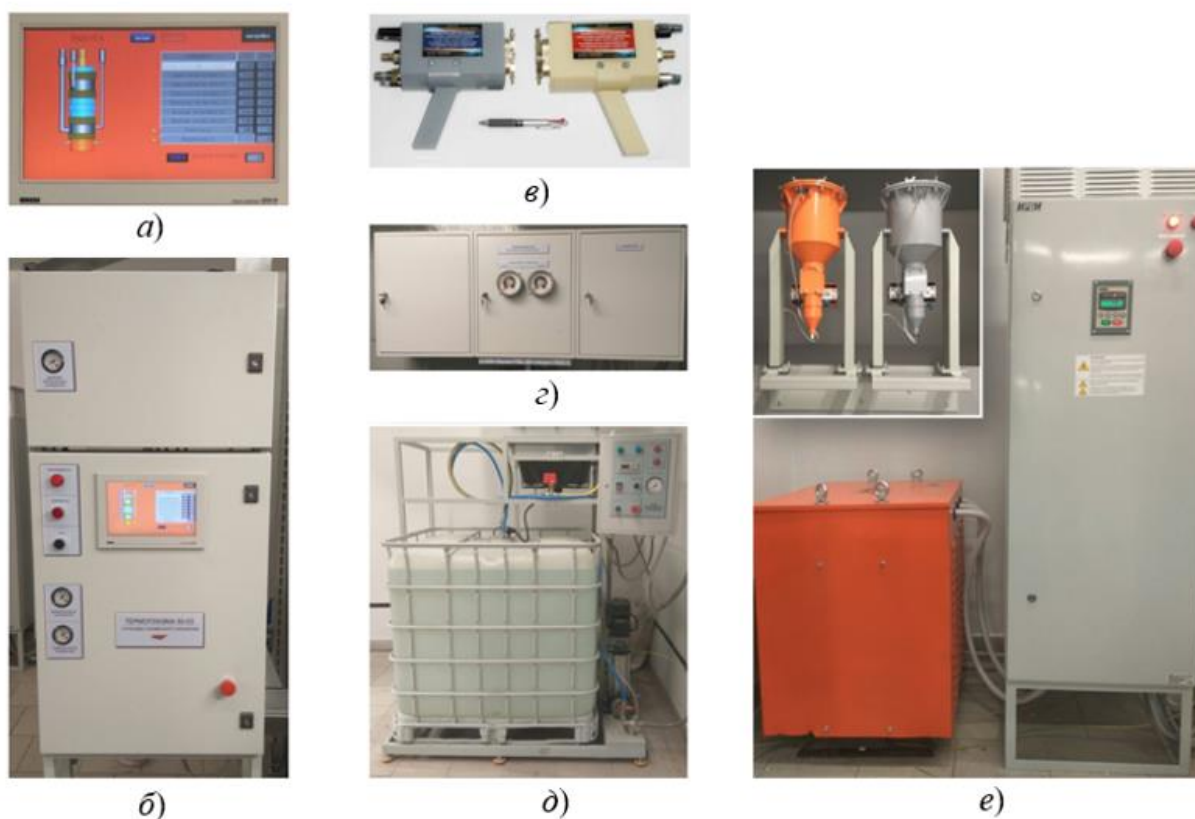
Внешний вид элементов установки плазменного напыления «Термоплазма 50-03»:
